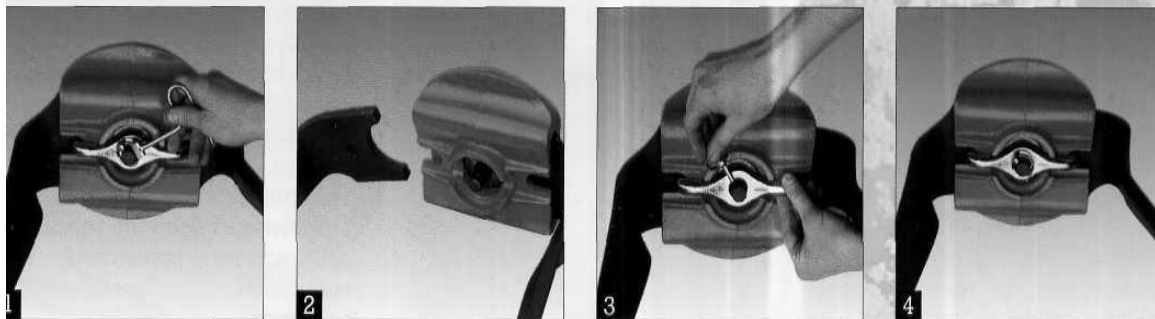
Вид механизма быстросъемного крепления ножей
